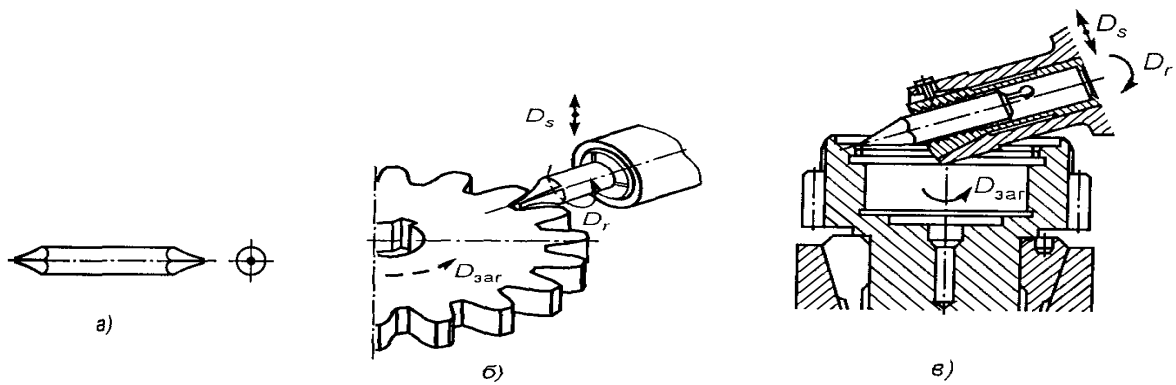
Схема пальцевой фрезы для закругления торцов зубьев шестерен
